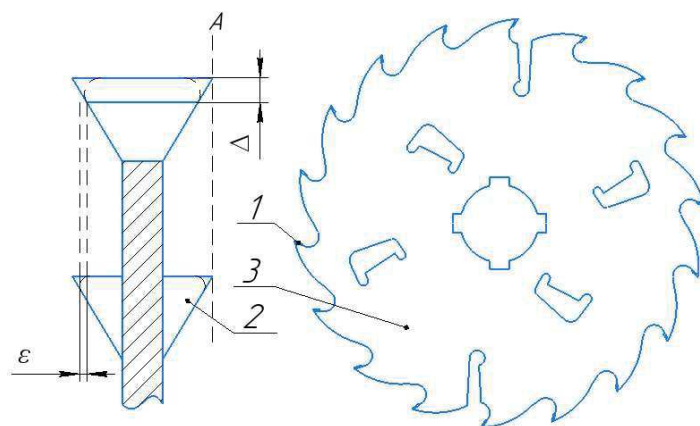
Плоскости движения зуба пилы и стабилизатора
